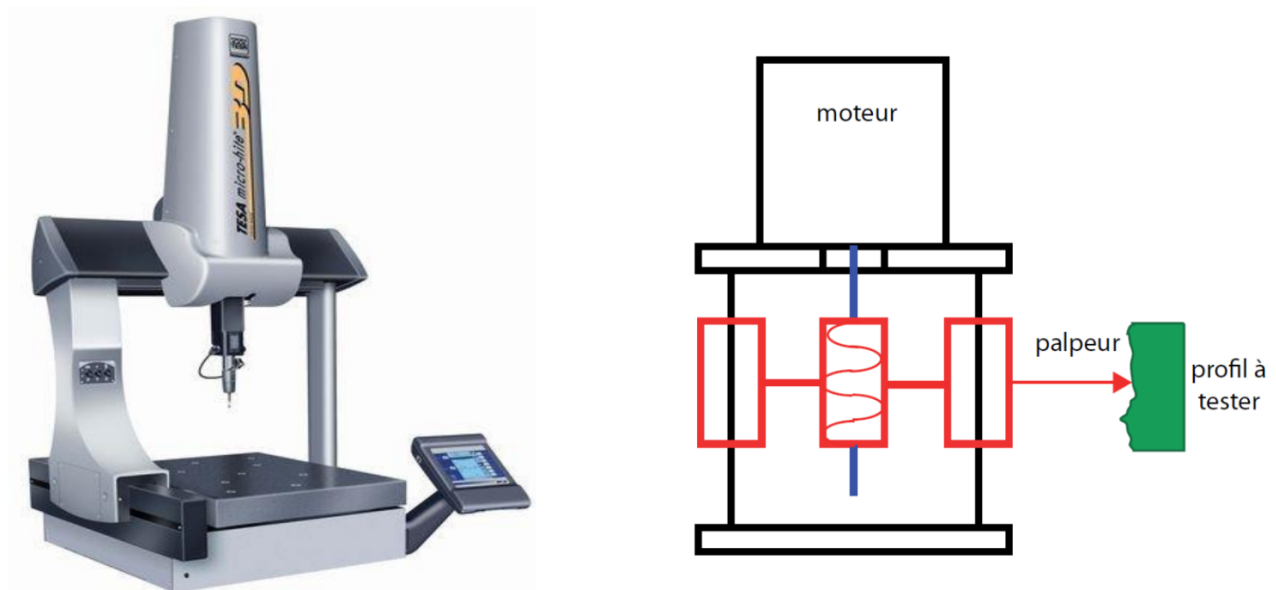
Machine à mesurer tridimensionnelle et modèle cinématique associé.
